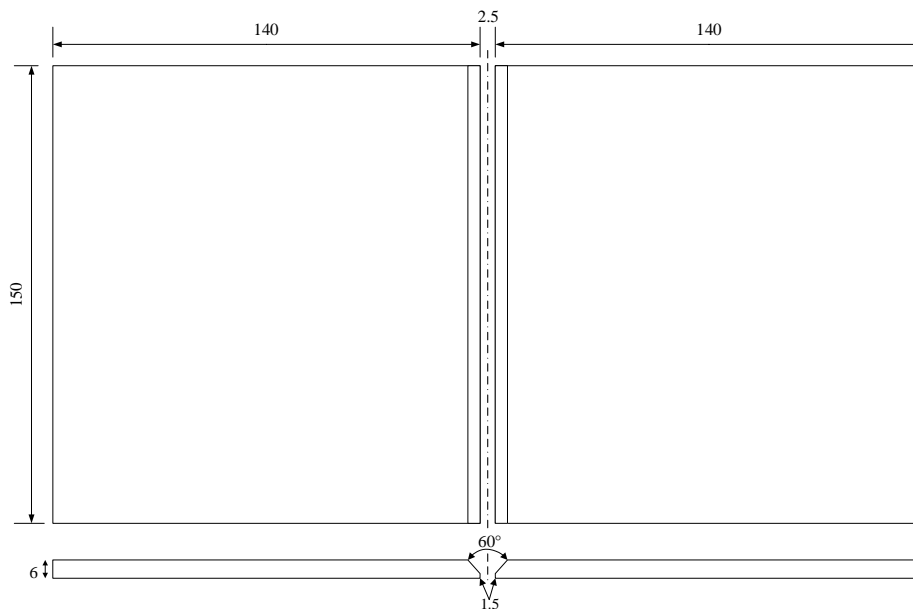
Géométrie de l'éprouvette de soudure bout à bout
